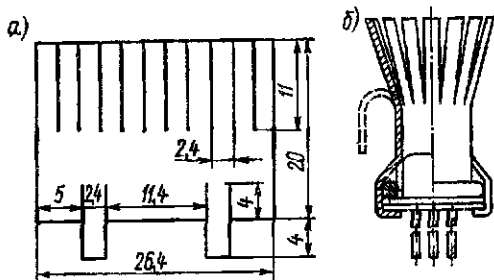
Радиатор для маломощного транзистора: а — развертка; б — общий вид
